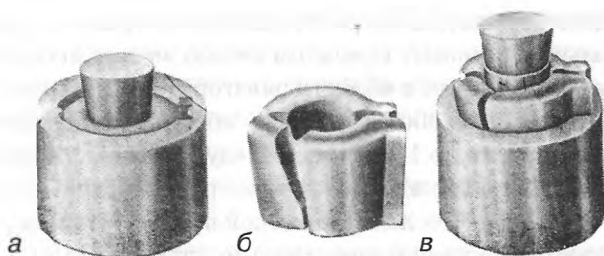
Комбинированная штамповка коронки металлическим штампом в металлическом контрштампе:
